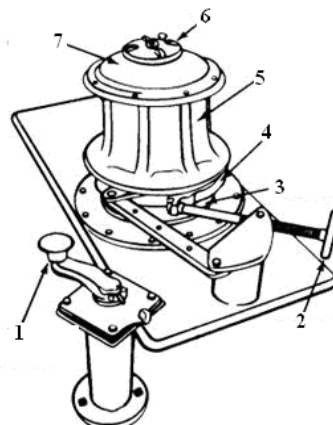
Cabestan : 1- controler; 2- mânerul frânei; 3- barbotină; 4- frână cu bandă; 5- tamburul cabestanului; 6- acționarea de control al cuplajului; 7- învelișul tamburului
